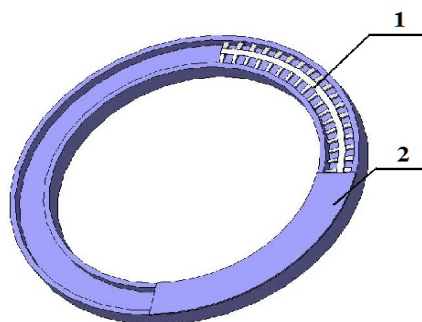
Пьезоподушка: 1 – пакет пьезоэлементов; 2 – упругий корпус
